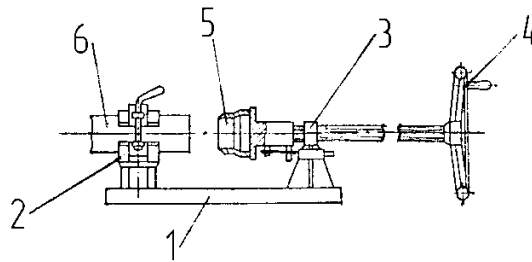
Устройство для формования буртов и раструбов: 1 - основание; 2 - зажим; 3 - передача винт-гайка; 4 - штурвал; 5 - пуансон; 6 - обрабатываемая труба
